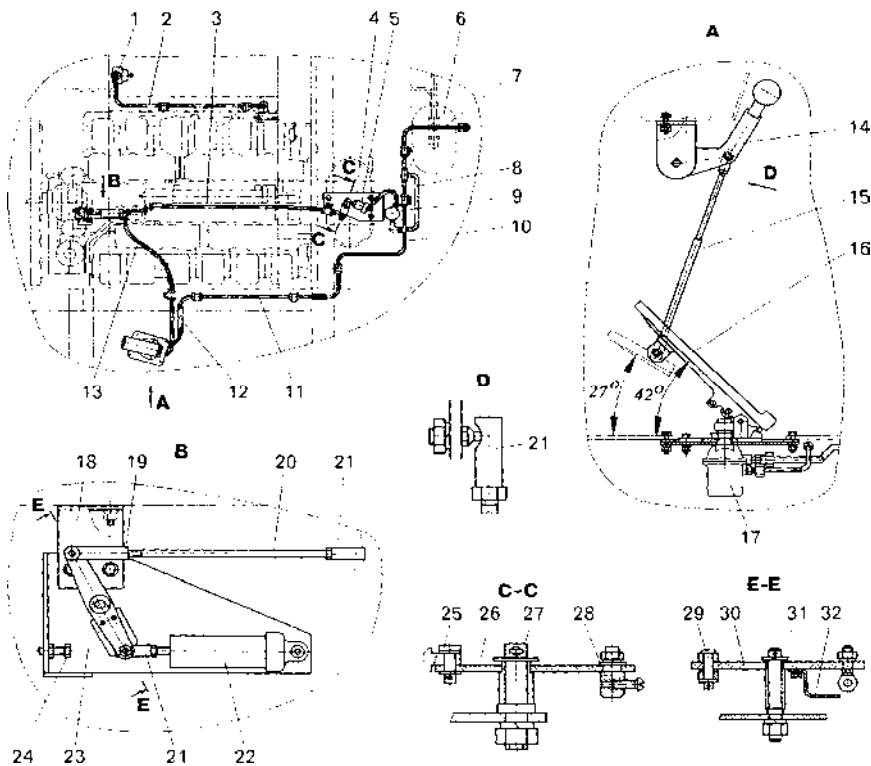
Привод управления подачей топлива самосвала БелАЗ-7555А:
